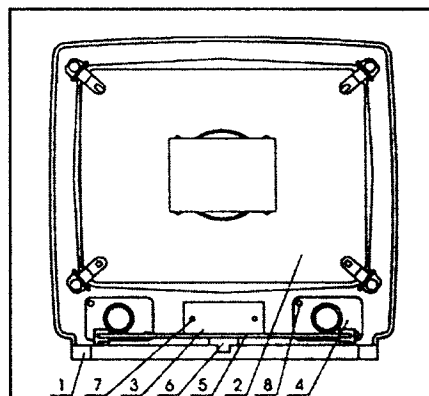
Вид телевизора "Витязь 51 CTV 6623T" сзади со снятым кожухом: 1 — корпус; 2 — блок кинескопа; 3 — модуль управления; 4 — плата моношасси; 6 — кронштейн; 7 — винт 3x10,5; 8 — шуруп 2-4x16,05
